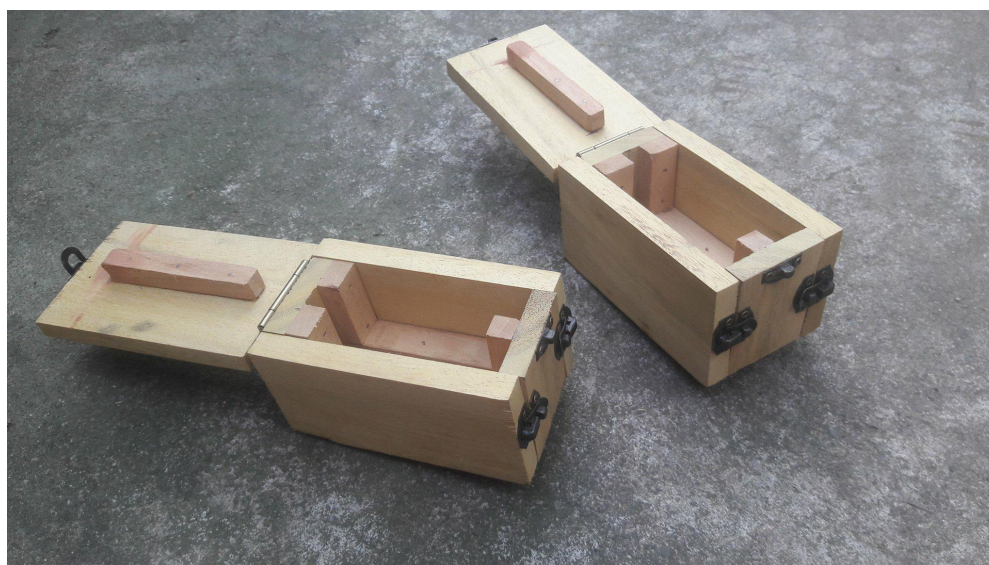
Molde de Ladrillo N° 2, Fuente: Autor
